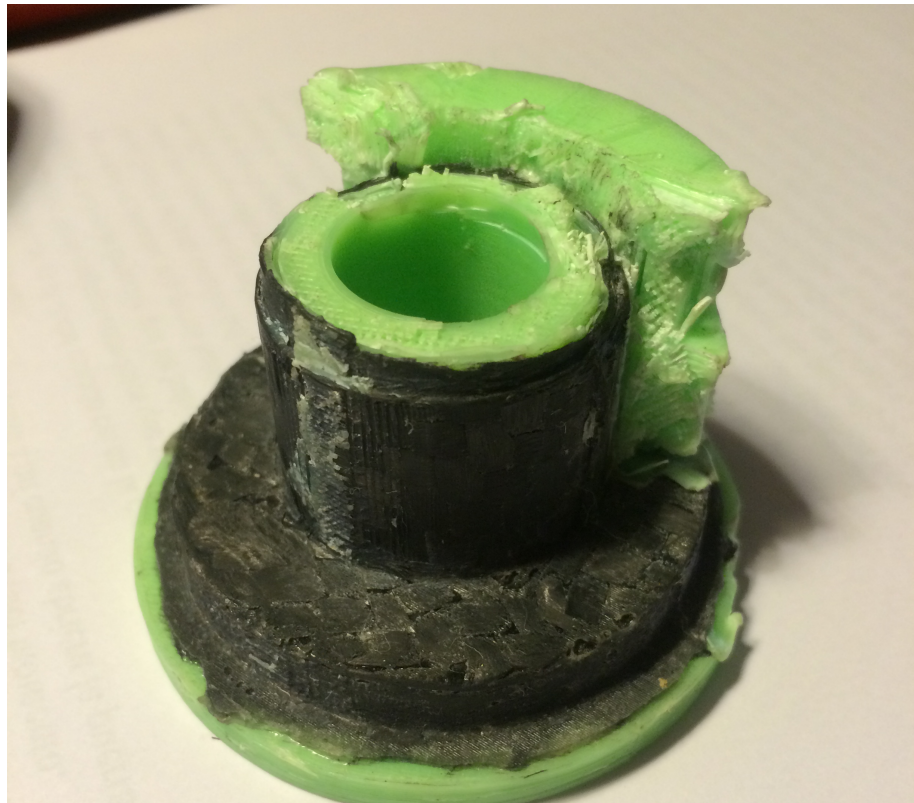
Desmoldeo buje. Estado del molde del buje después de la rotura de una parte del molde exterior. (Fuente: Propia)
